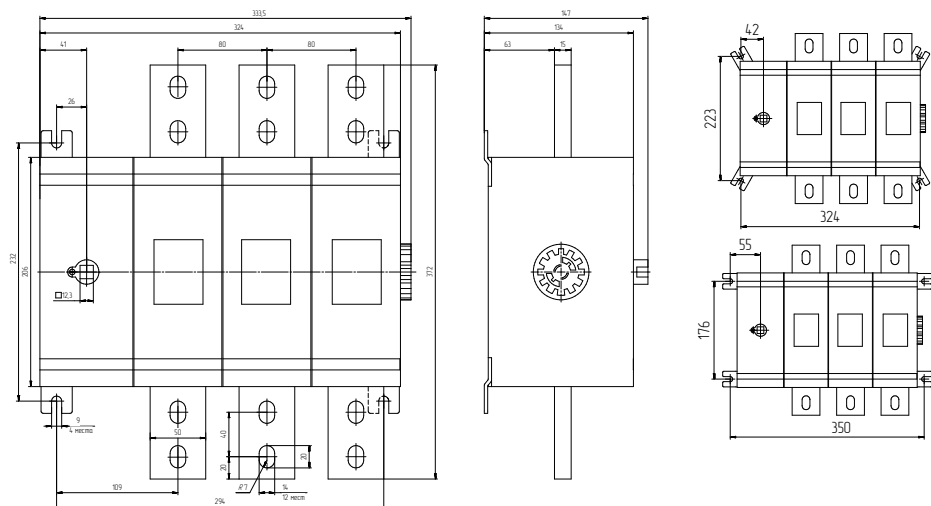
Выключатель-разъединитель 1600 А стандартного исполнения
